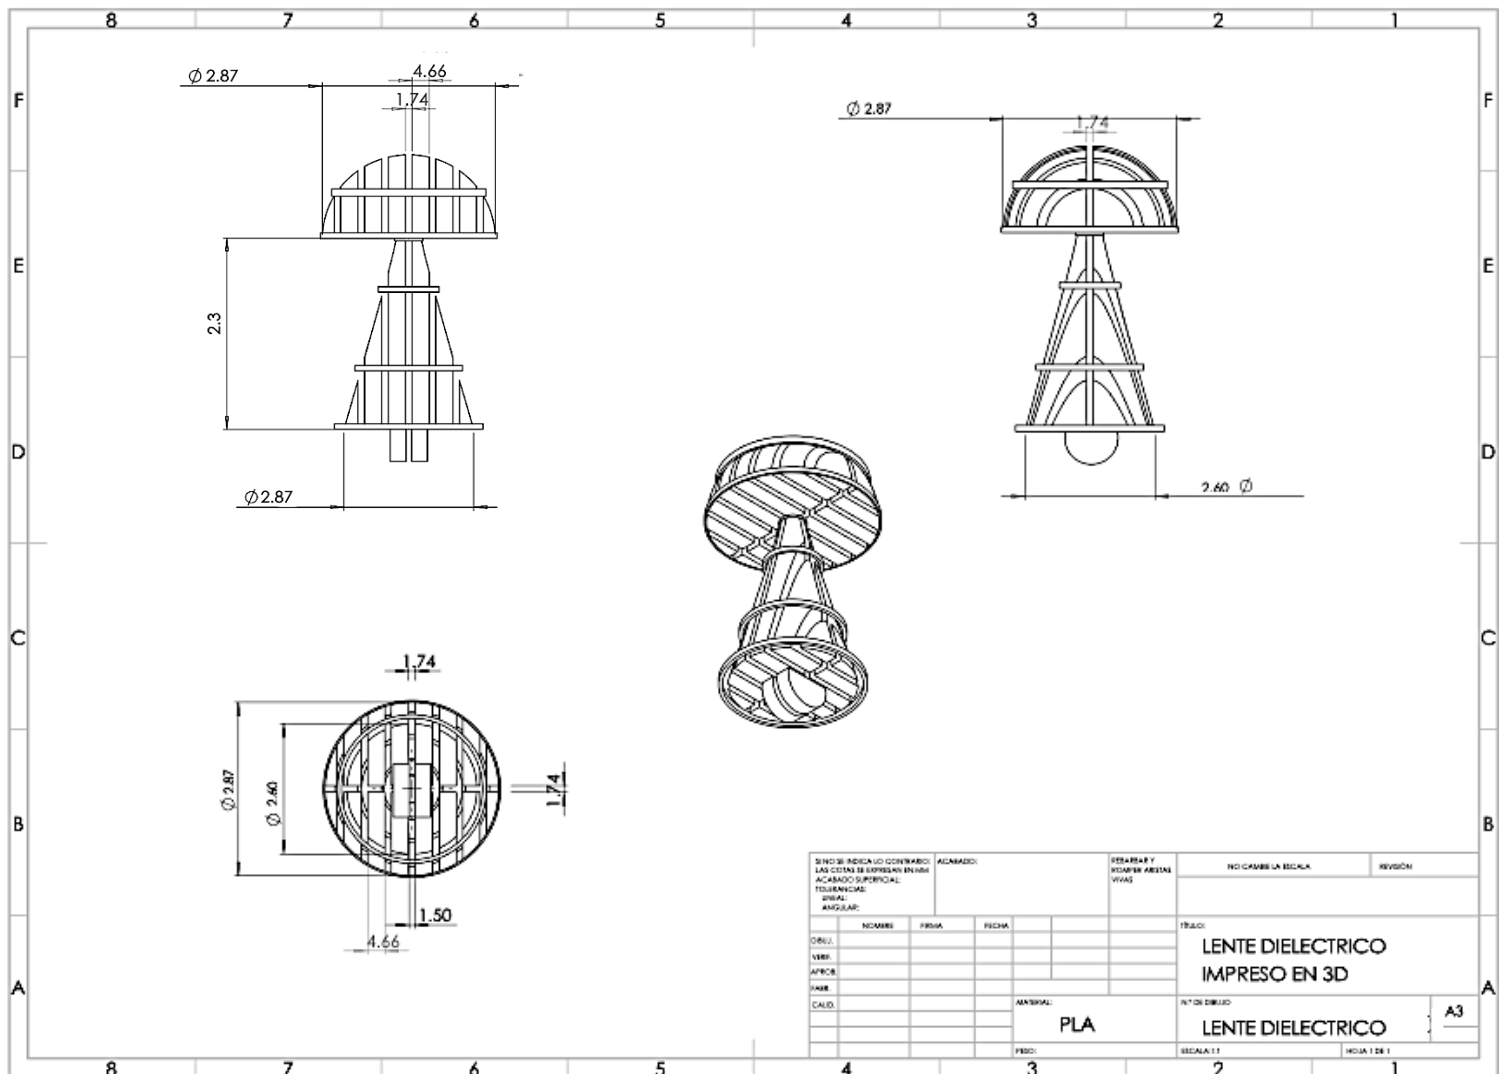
Dibujo técnico diseño del lente dieléctrico realizado en solidworks
